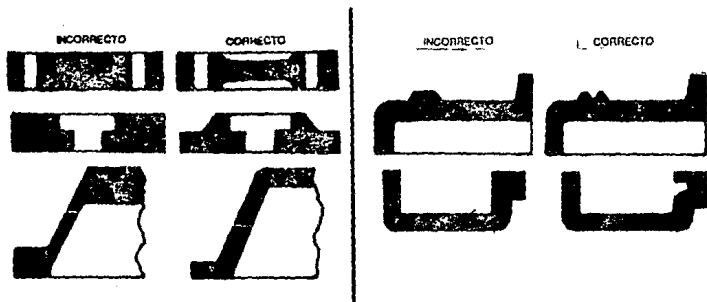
Alternativas de diseño para mantener un espesor uniforme de la sección del producto. (Ref. 5).
